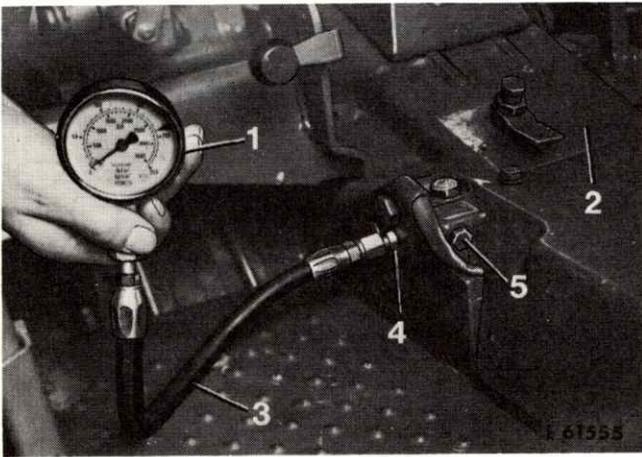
Manomètre haute pression branché sur le relevage hydraulique
